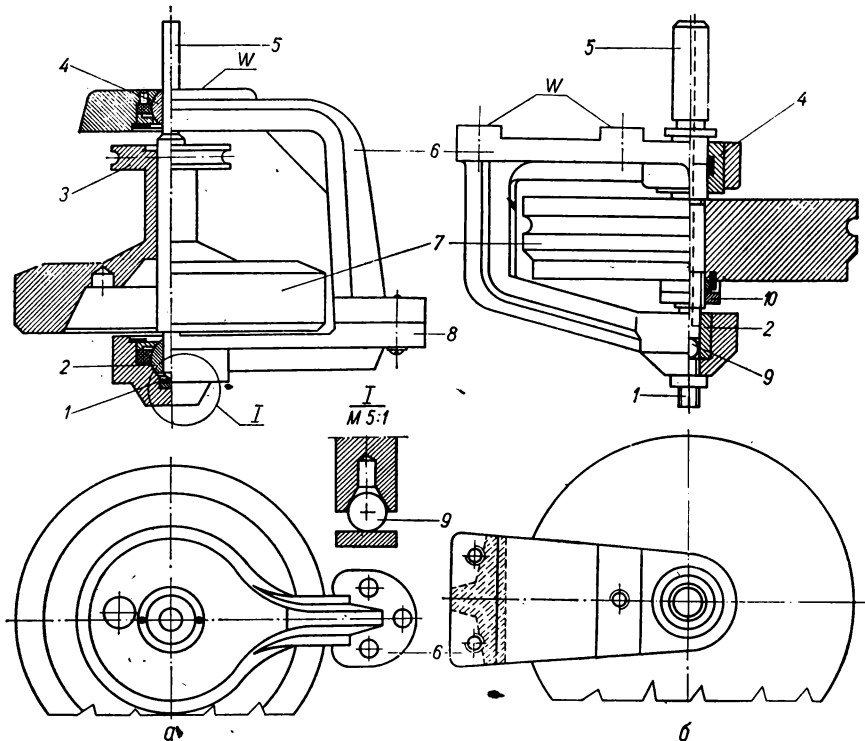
Конструкции узлов ведущего вала исполнения VI.
